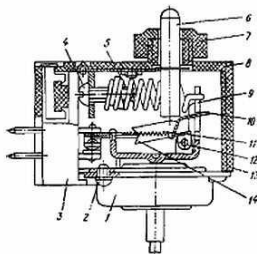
Конструкция прибора полуавтоматического управления оттаивания ТО-11: 1 — термочувствительная система; 2 — винт; 3 — колодка; 4 — винт настройки; 5 — пружина настройки точки срабатывания; 6 — кнопка; 7 — гайка; 8 — кожух; 9 — двуплечий рычаг; 10 — рычаг; 11 — опрокидывающаяся пружина; 12 — ось; 13 — корпус; 14 — рычаг резкого размыкания контактов.
